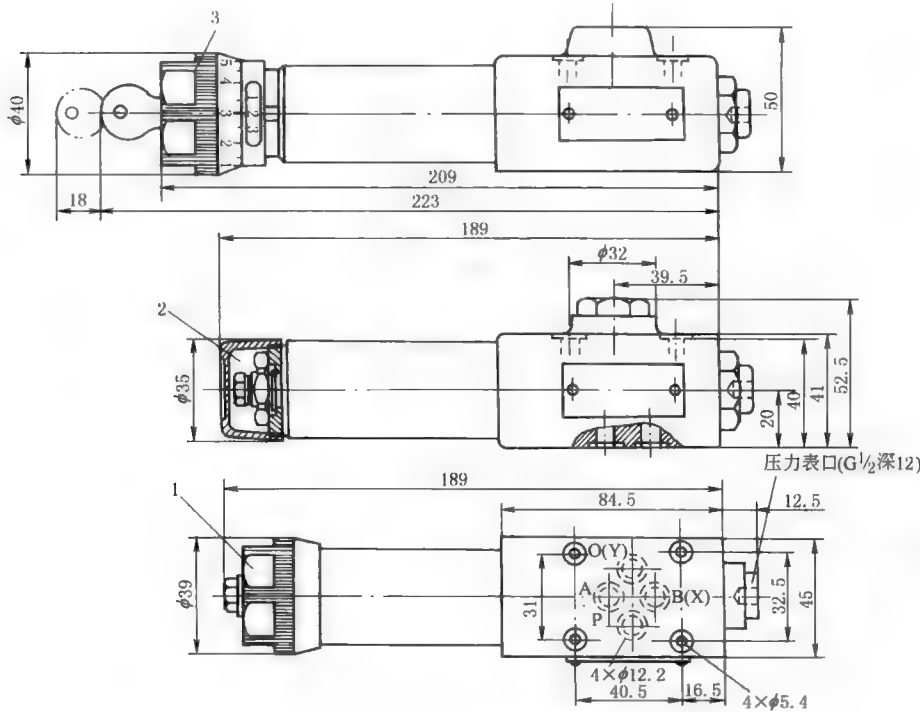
DZ6DP 型直动式顺序阀外形尺寸
